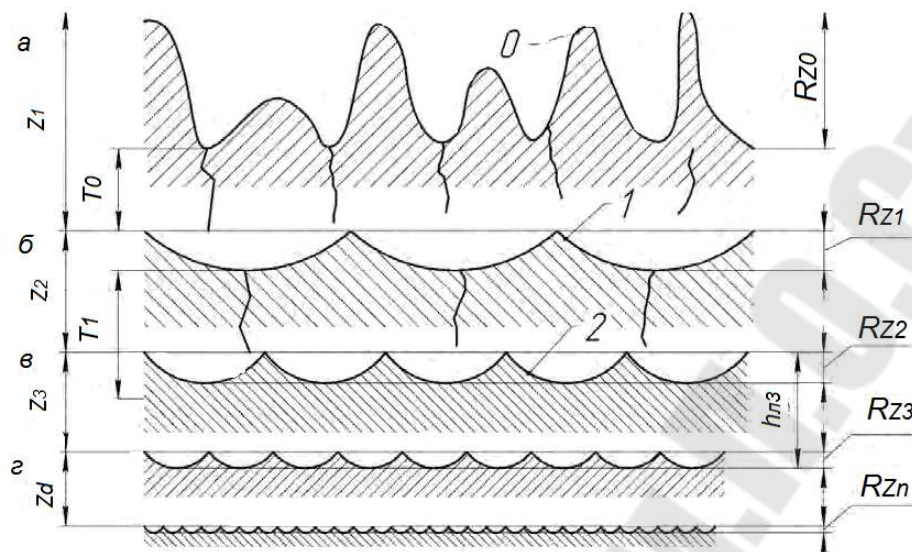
Схема удаления материала заготовки последовательными проходами
